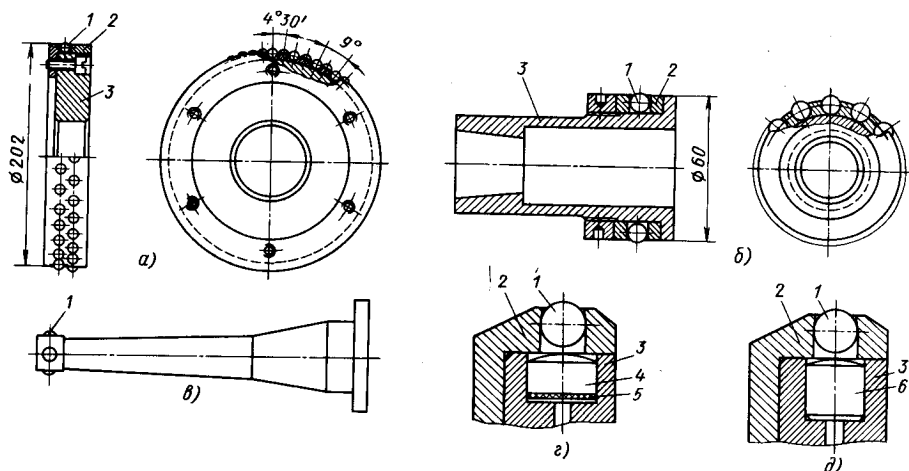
Инструмент для центробежной обработки: а — для плоскостей с двухрядным расположением шариков; б и в — для отверстий; г и д — инструмент с отражением шариков; 1 — шарики; 2 — сепаратор; 3 — корпус; 4 и 6 — отражатели шариков плавающий и неподвижный; 5 — резиновый буфер
